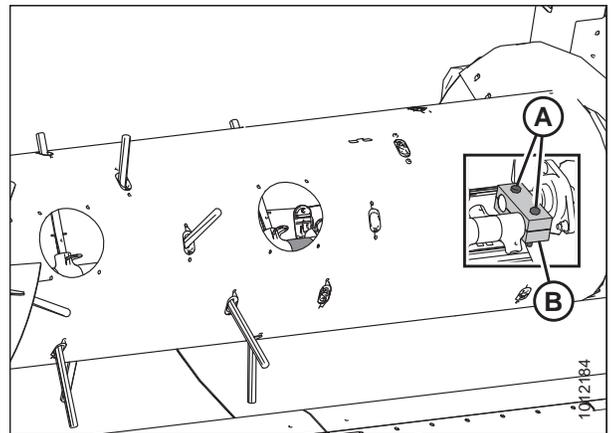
Abrazadera de soporte de dedos de sinfín del lado izquierdo - Se muestra la imagen del corte
